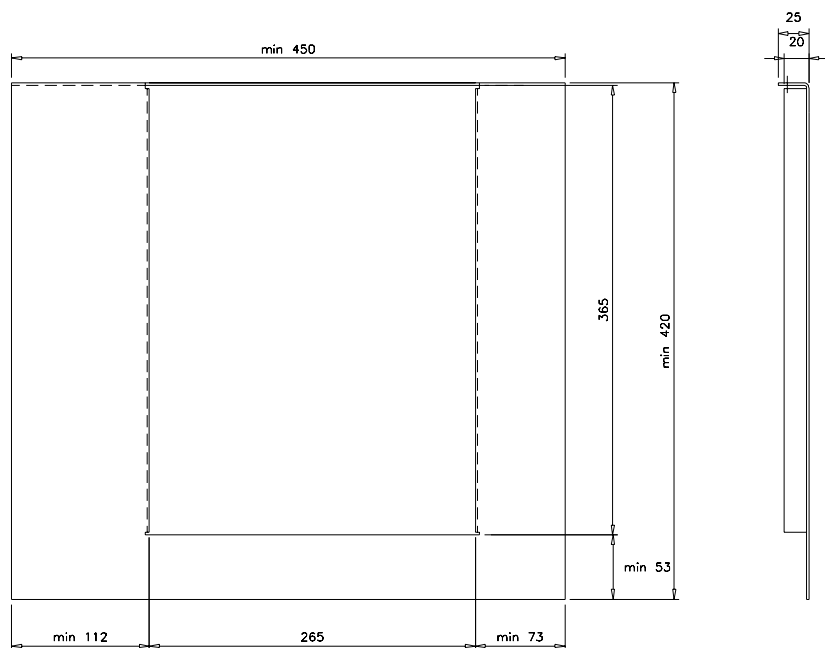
外形尺寸 B3 供电模块的空气挡板
